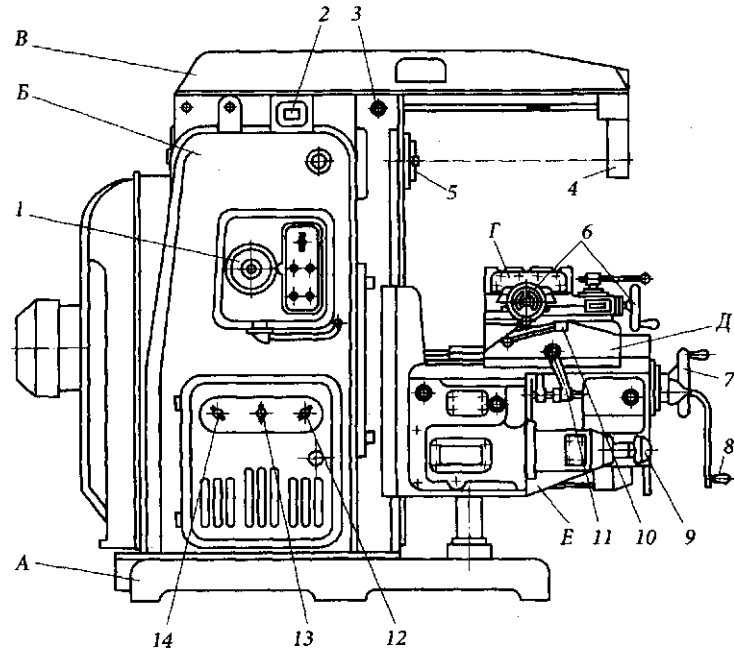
Консольный горизонтально-фрезерный станок:
